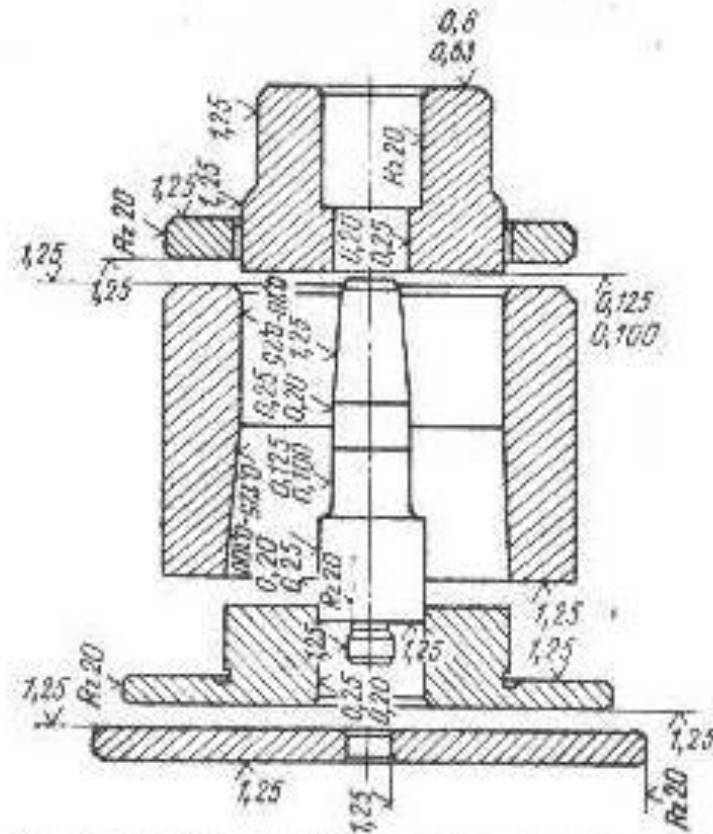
Шероховатость поверхности основность поверхности основных деталей пресс-формы
